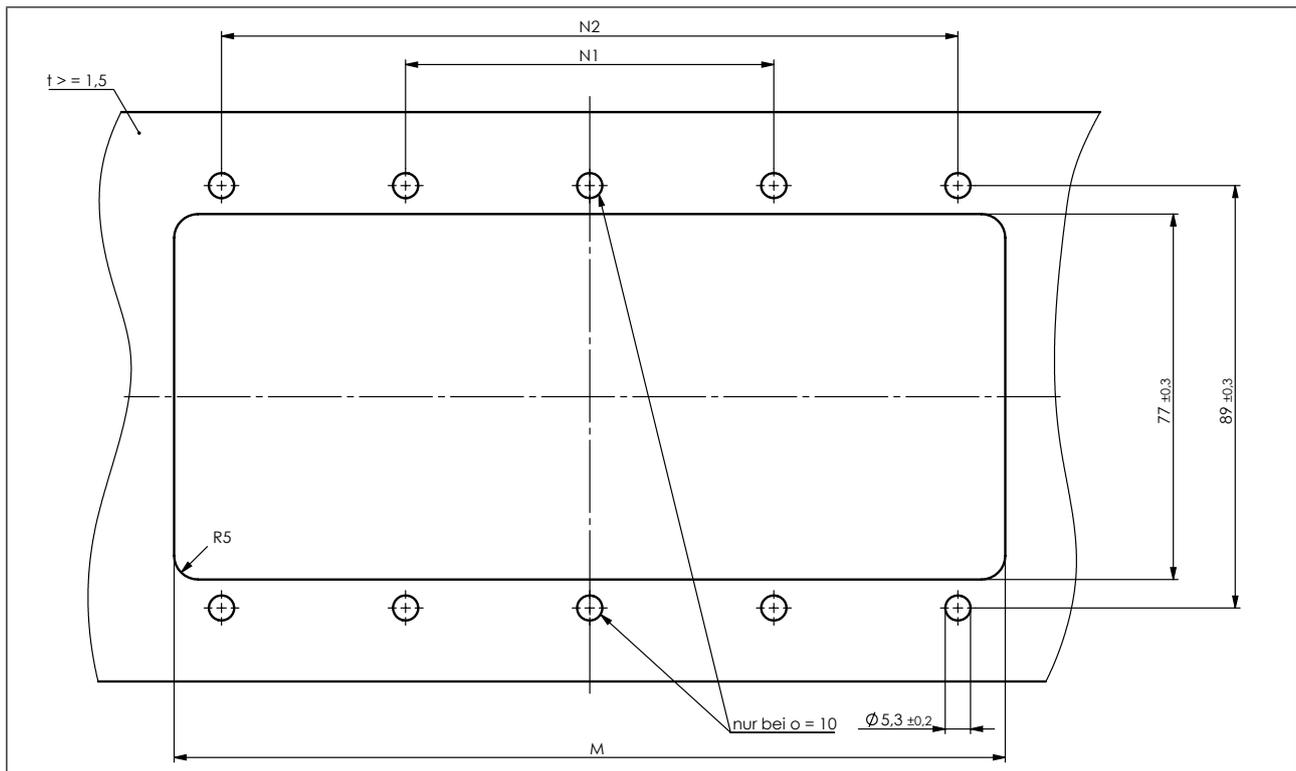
Flanschbild AirLINE Quick – Maße siehe „Tabelle 1“
